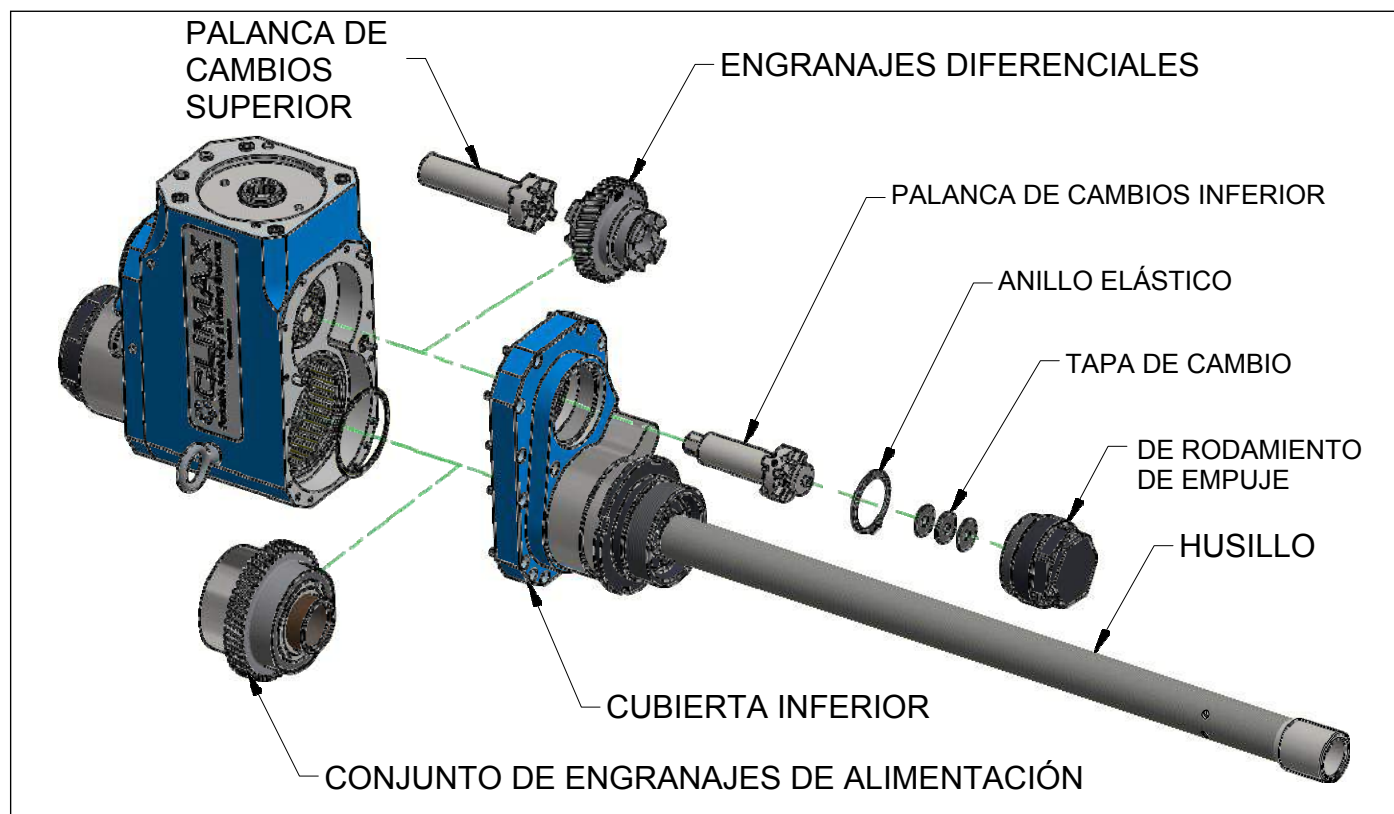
REENSAMBLAJE DE LA CAJA DE ENGRANAJES
